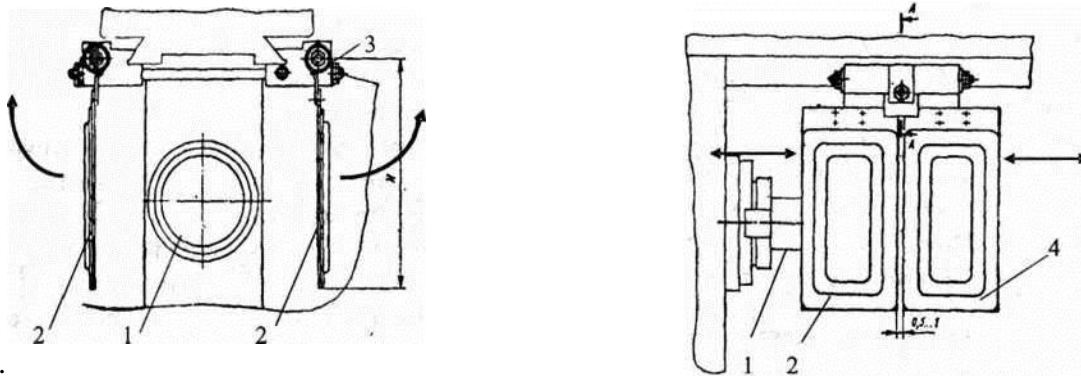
Защитный экран универсального фрезерного станка: 1 - шпиндель; 2 - защитный экран; 3 - шарнир; 4 – смотровое окно.
